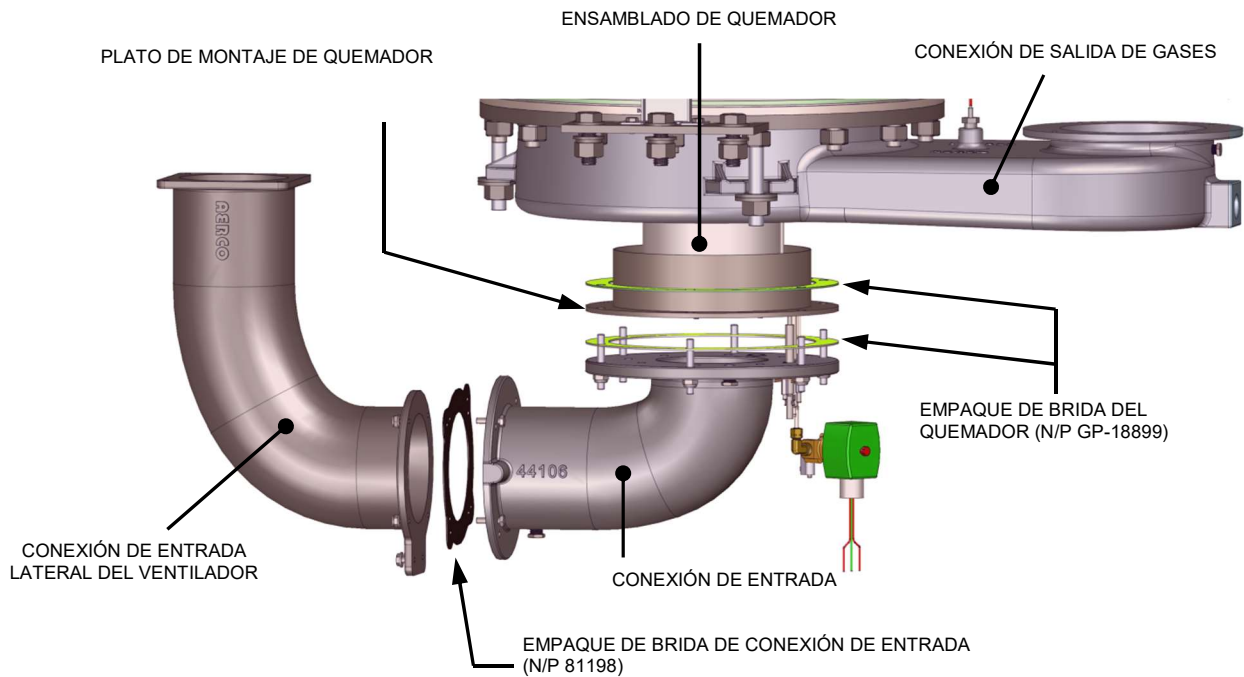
Conexión de entrada y quemador - Corte transversal con vista detallada
